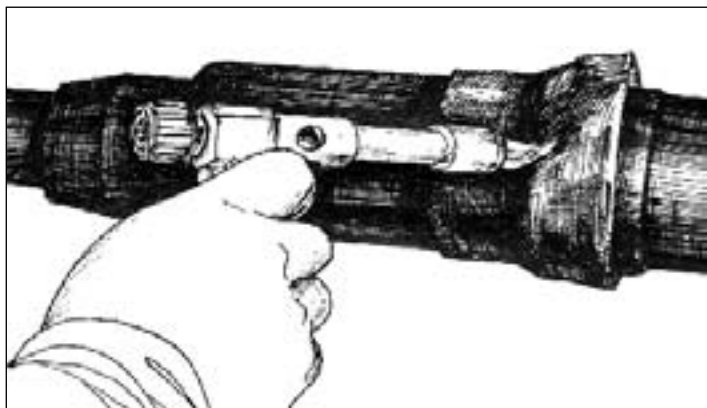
Усадка трубки ТУТ на среднем стыке
